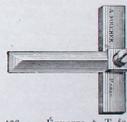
Équerre à T forte en acier, à branche mobile. . 18 fr.
